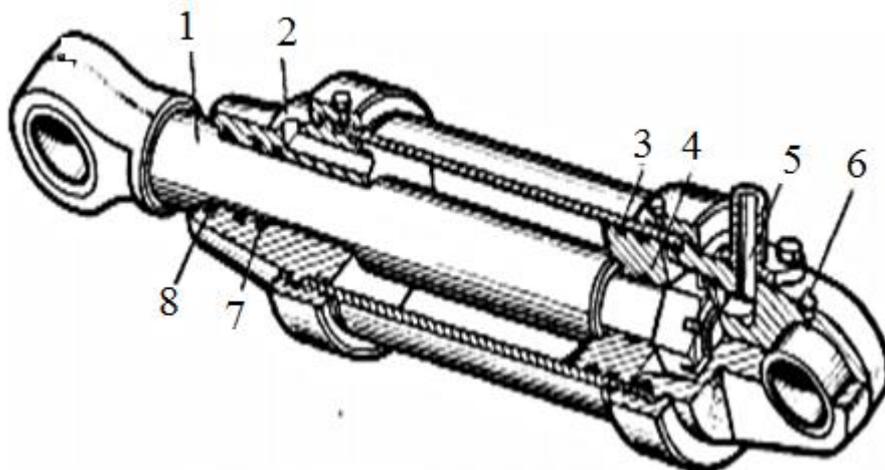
Конструкция гидроцилиндра: 1-шток; 2-крышка; 3,7 и 8-резиновые манжеты; 4-поршень; 5-штуцер; 6-крышка с отверстием.
